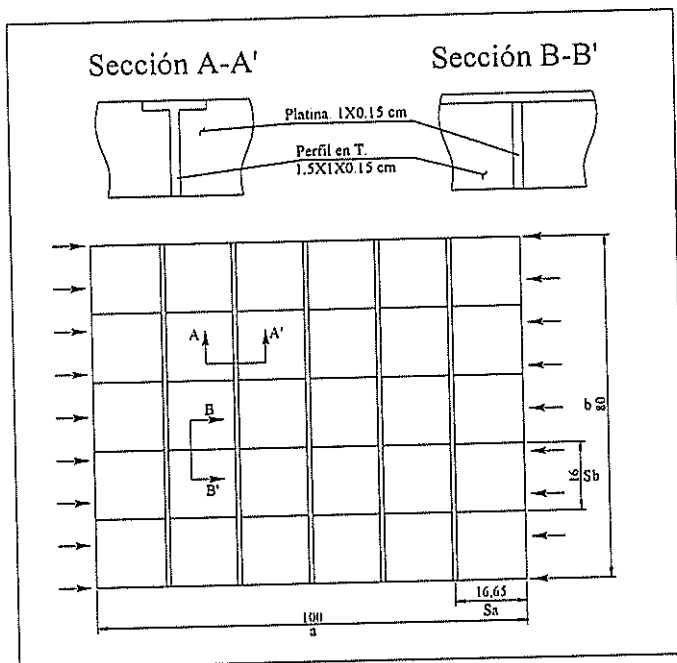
Esquema de plancha con refuerzos en las dos direcciones.
